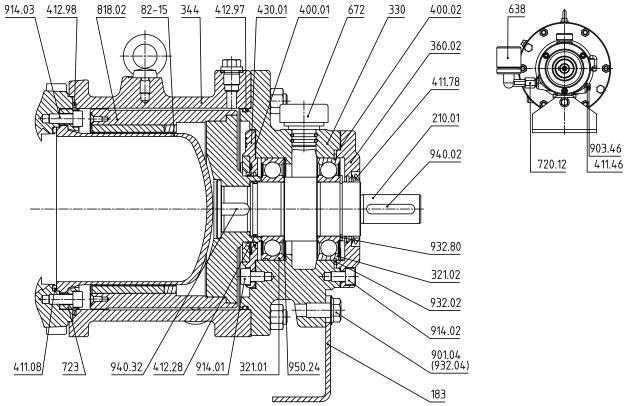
Ausführung Lagerträger mit Ölschmierung und Wellendichtring als Leckagebarriere
